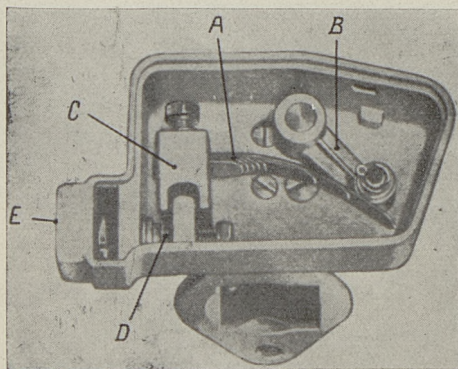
Mechanizm sprężynowy regulatora Handy.
